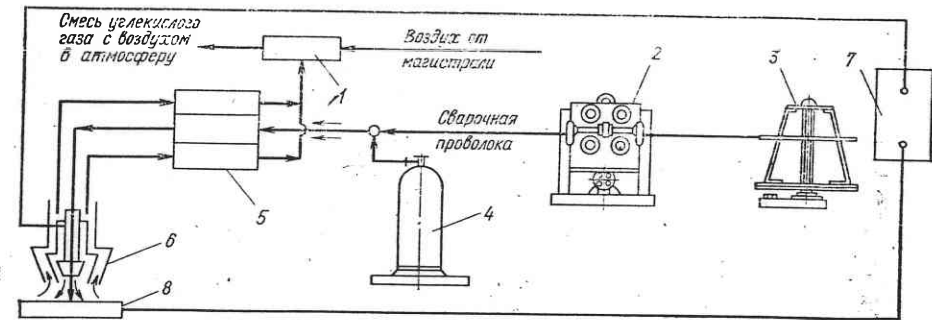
Схема устройства для местного отсоса газа из зоны сварки: 1 — инжектор; 2 — подающий механизм; 3 — бухта; 4 — баллон; 5 — шланг; 6 — горелка; 7 — источник питания; 8 — изделие
